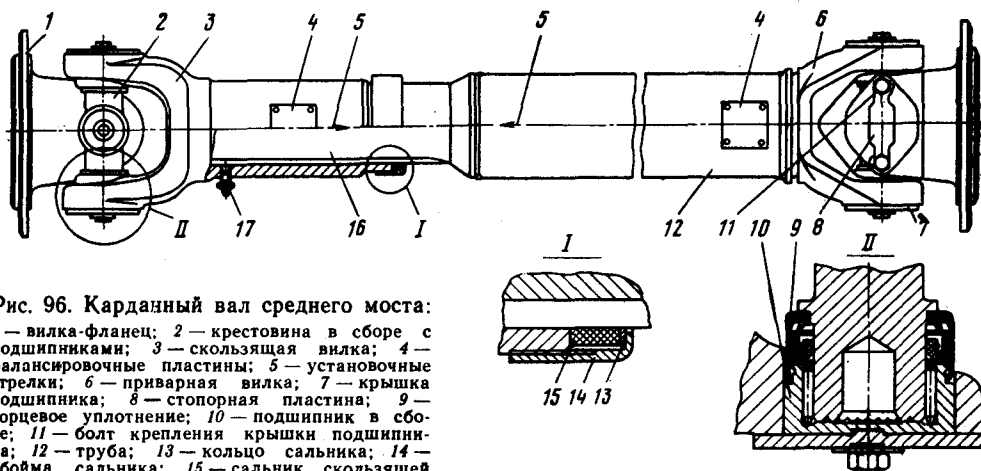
Карданный вал среднего моста: 1 — вилка-фланец; 2 — крестовина в сборе с подшипниками; 3 — скользящая вилка; 4 — балансировочные пластины; 5 — установочные стрелки; 6 — приварная вилка; 7 — крышка подшипника; 8 — стопорная пластина; 9 — торцовое уплотнение; 10 — подшипник в сборе; 11 — болт крепления крышки подшипника; 12 — труба; 13 — кольцо сальника; 14 — обойма сальника; 15 — сальник скользящей вилки; 16 — шлицевой конец; 17 — масленка
